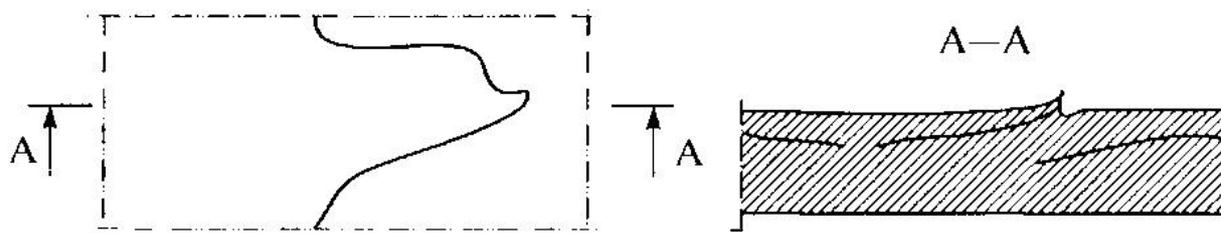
Отслоение по сечению сварного шва
